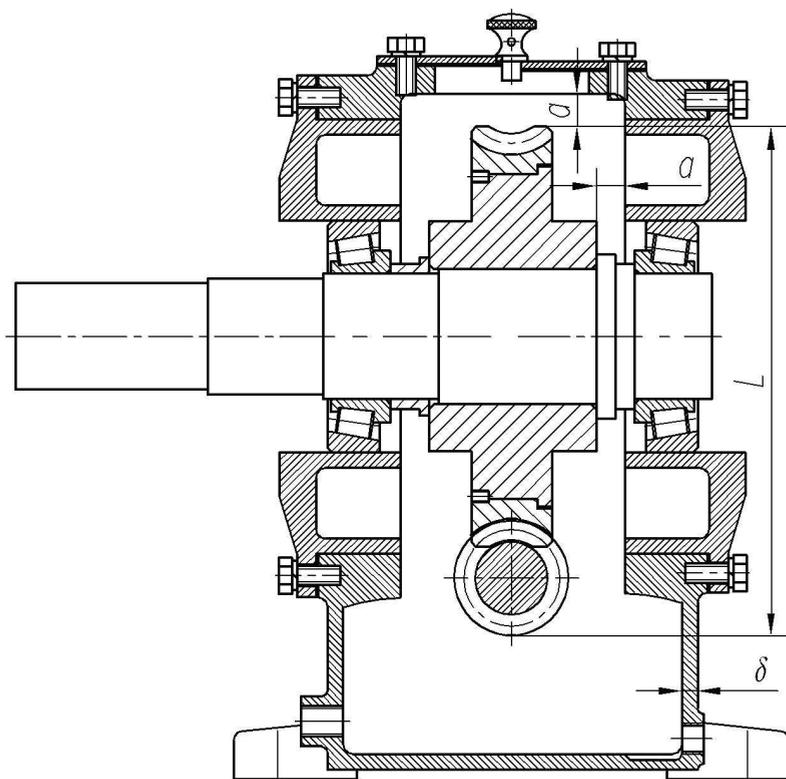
Корпус червячного редуктора с осевой сборкой
